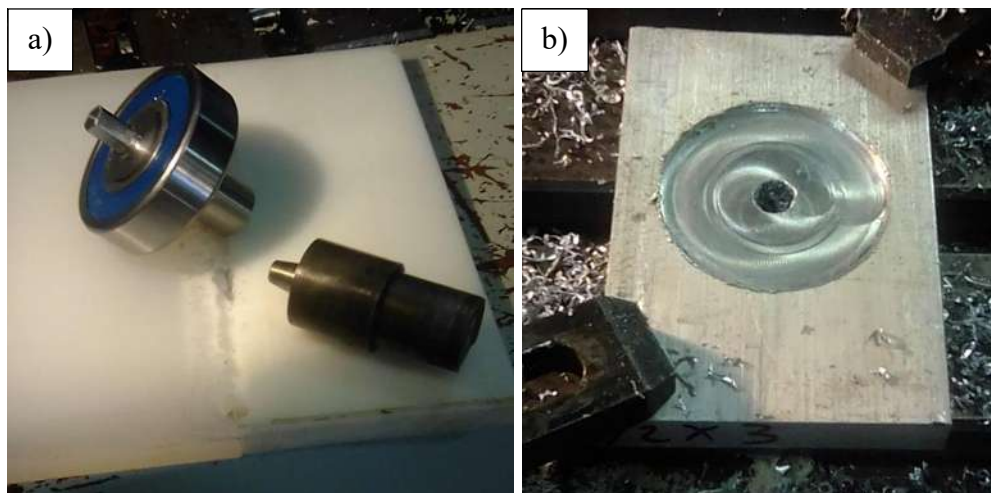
a) Herramienta insertada en el balero, b) placa de aluminio 6061-T6 con preparación para insertarse en el balero.
